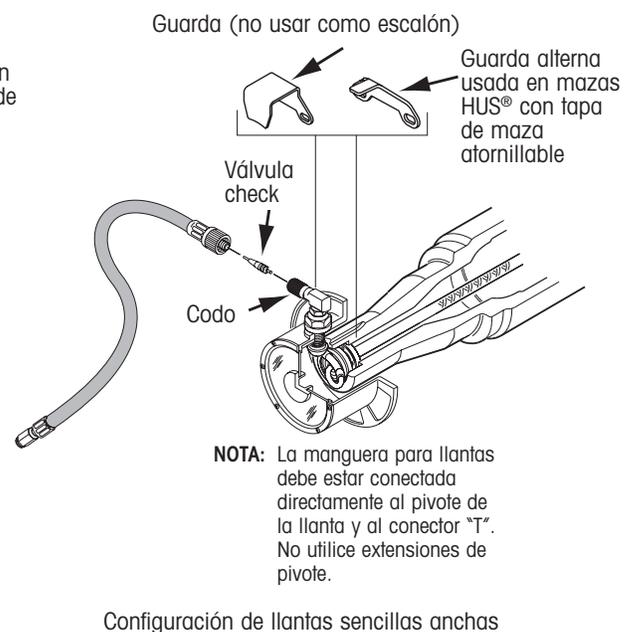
Instale la manguera para llantas en el pivote de la llanta
